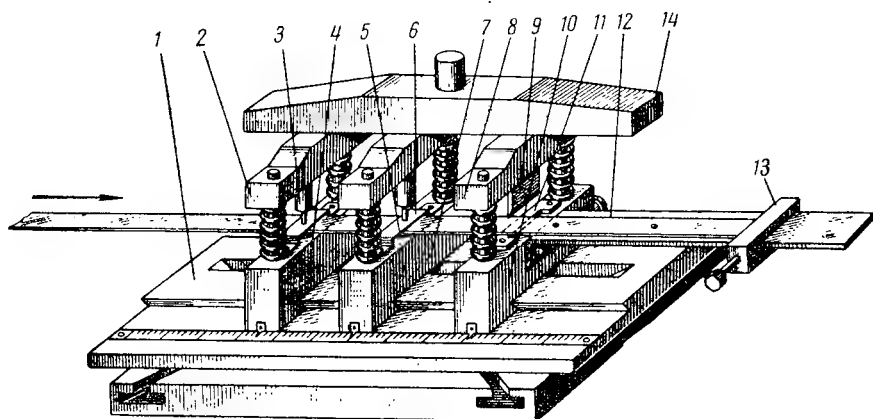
Комбинированный штамп для одновременной отрезки одной заготовки петушка и вырубке отверстий в другой заготовке петушка
